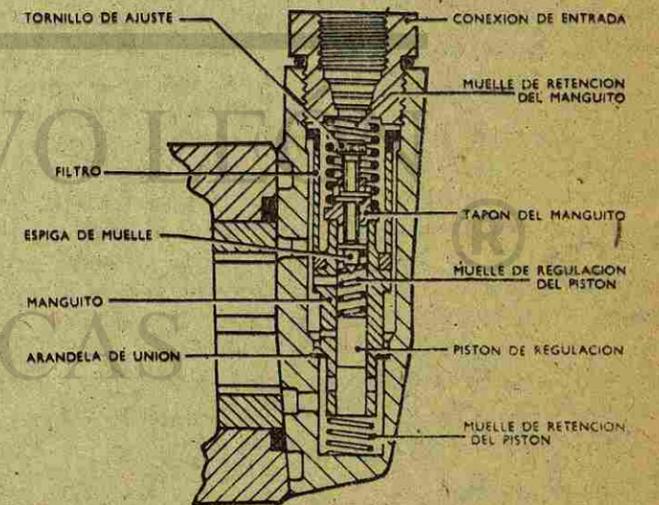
Placa de extremo con ajustador de presión de trasiego atornillado
